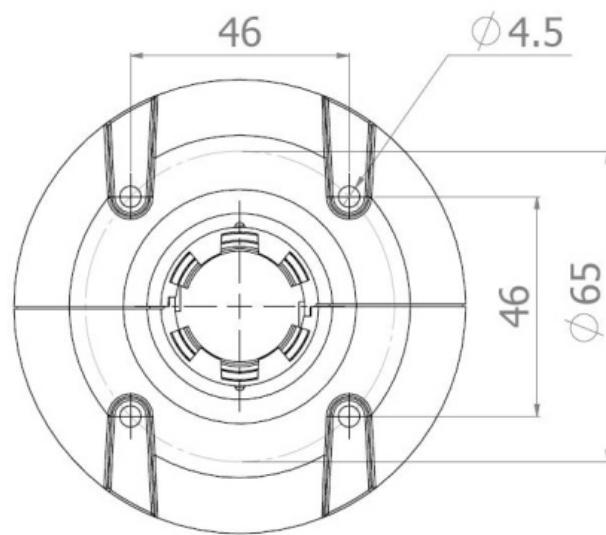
Размеры основания стойки и расположение отверстий для её крепления.
